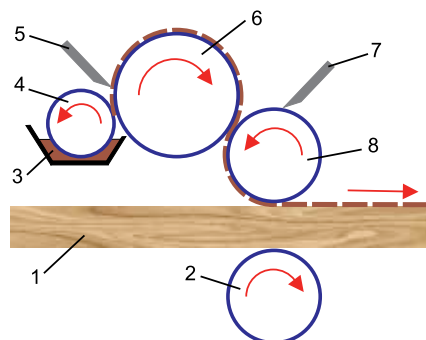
Схема печатного станка: 1 – деталь, 2 – подающий валик, 3 – ванна с печатной пастой, 4 – питающий валец; 5, 7 – очистные ракель, 6 – текстурный цилиндр, 8 – печатный цилиндр
